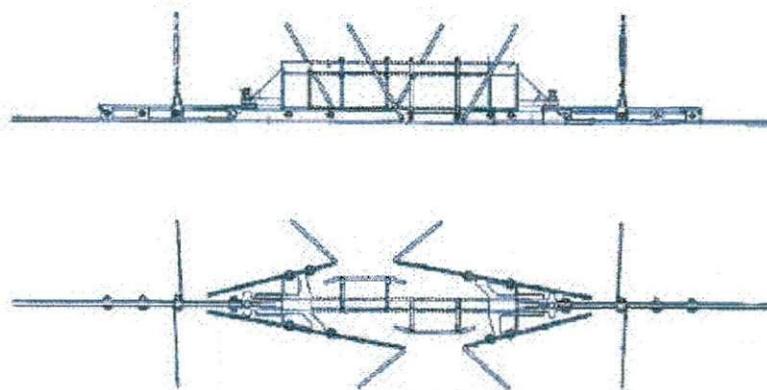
Desenho do isolador de seção 211625 da empresa Galland SARL.
